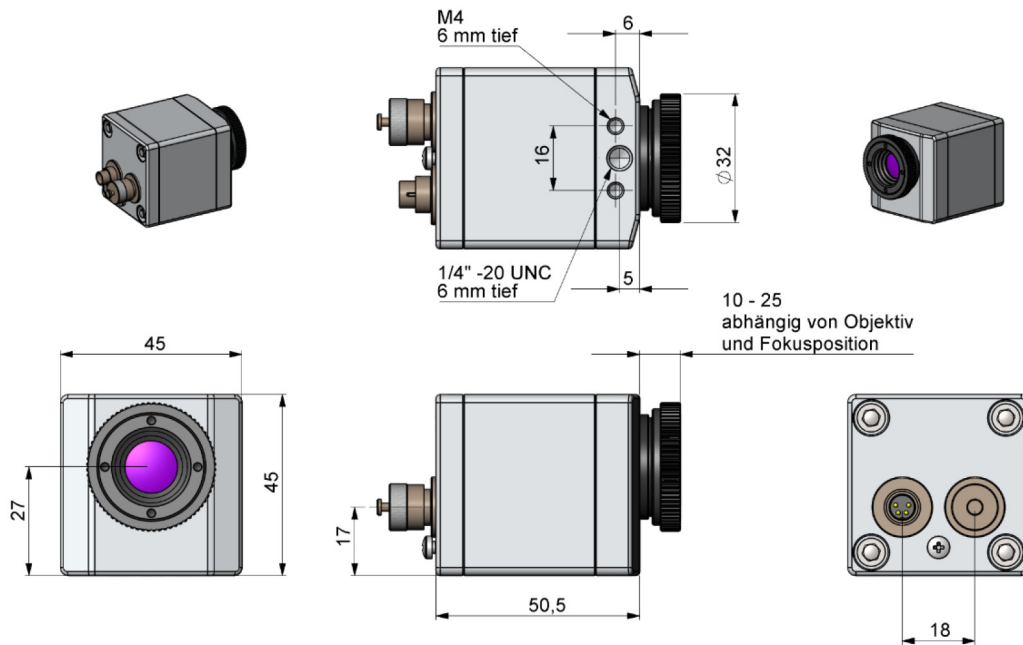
Maßzeichnung TIM 160S, Abmessungen in mm
